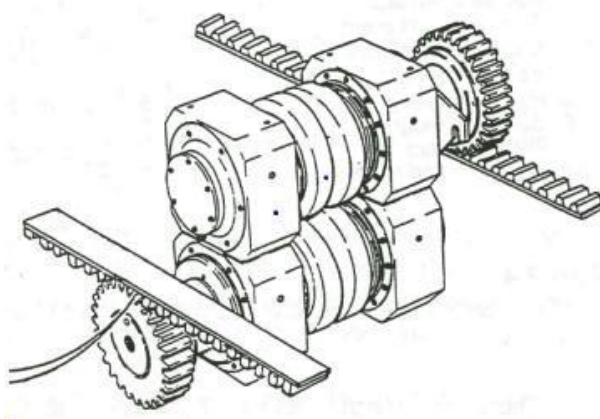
Схема приводу ведуча шестерня та нерухома рейка на сучасних станах холодної прокатки труб [2]
